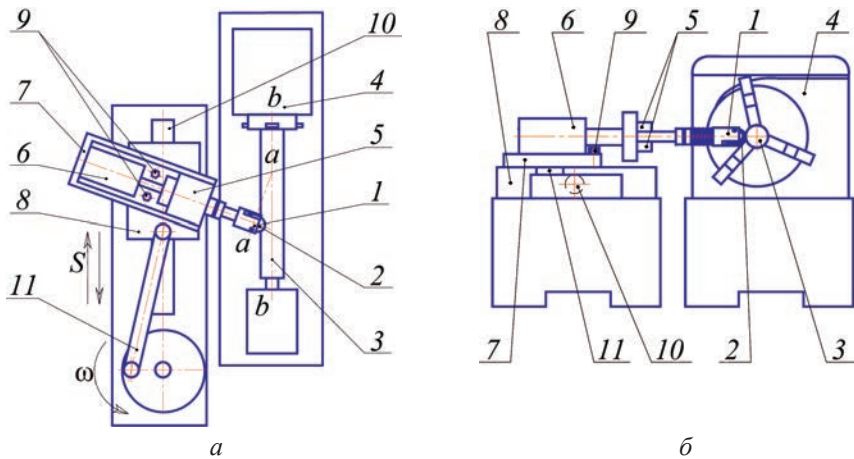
Стенд для ресурсных испытаний дисковых ножей рабочих механизмов для бестраншейной реконструкции трубопроводов по патенту РФ на полезную модель № 127465: *a* — вид сверху; *б* — вид спереди; 1 — вилка; 2 — дисковый нож; 3 — модель ветхого трубопровода; 4 — токарный станок; 5 — зажимы; 6 — гидроцилиндр; 7 — платформа; 8 — ползун; 9 — фиксирующие винты; 10 — направляющая; 11 — кривошипно-шатунный механизм
